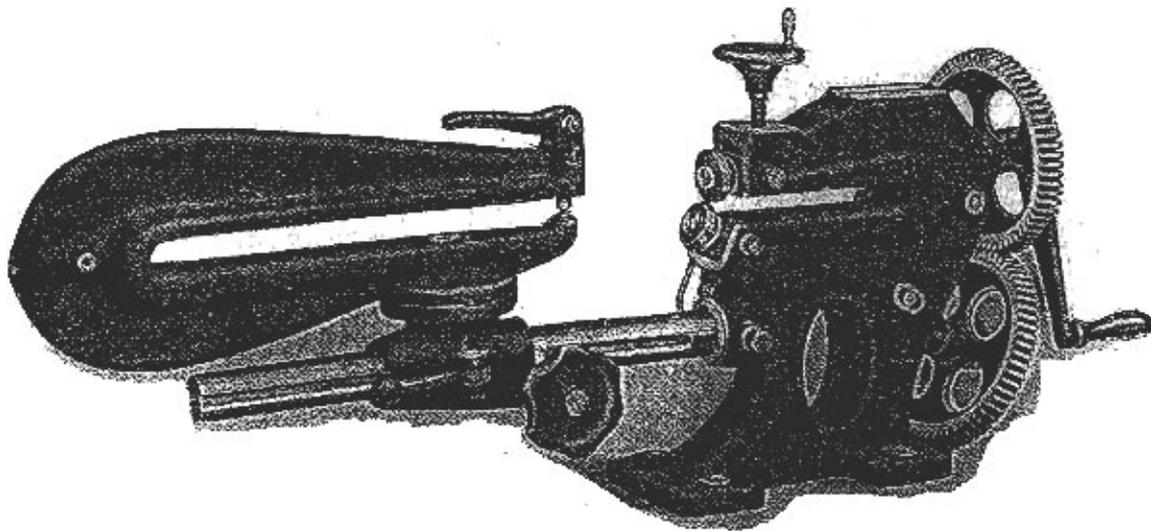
/3      Hilfsmaschinen des Karosseriebauers für die
